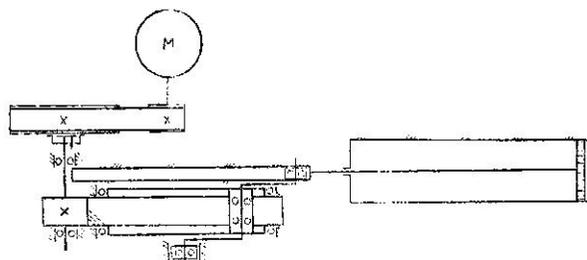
Кинематическая схема привода насосной установки ВНПБ-10/32
